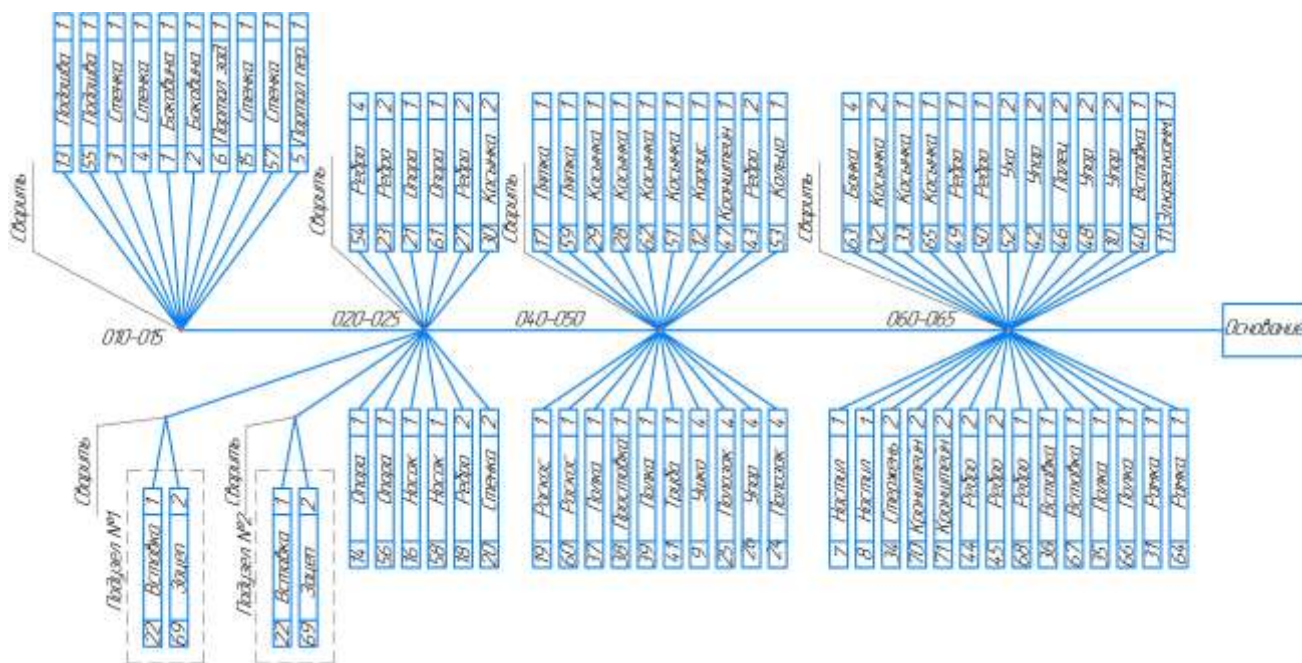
Технологическая схема сборки-сварки основания.
